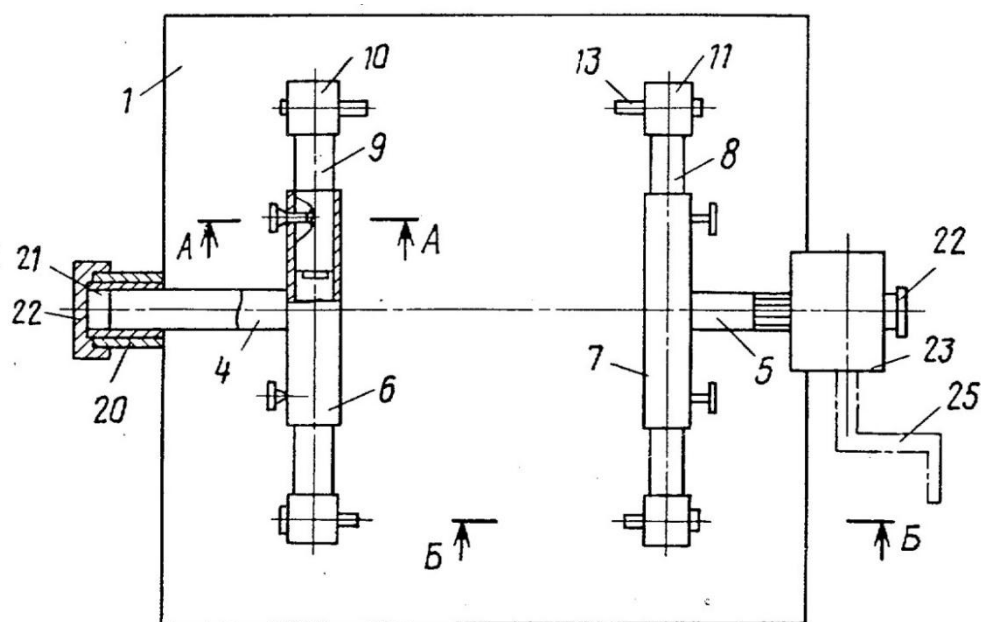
Стенд для разборки двигателей по а.с. № 770883
